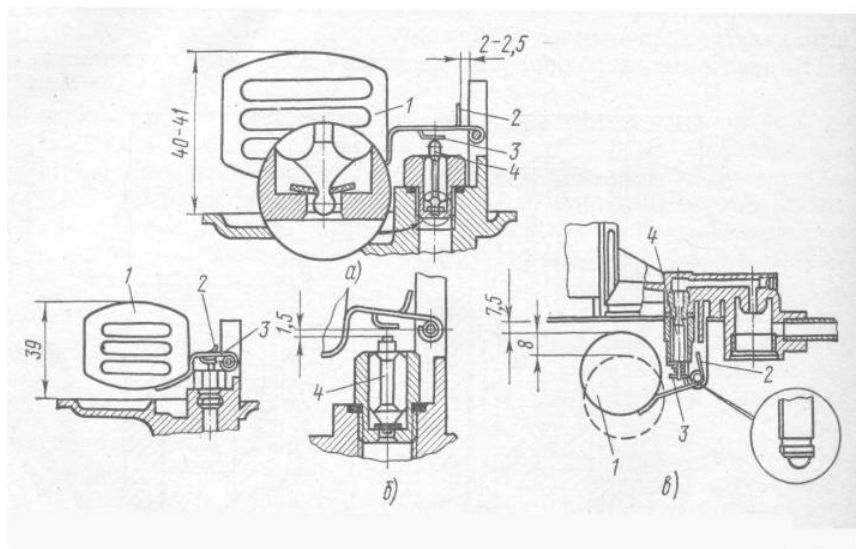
Регулировка уровня топлива в поплавковой камере карбюраторов: а – К-126Г, б – К-126Н, в – ДААЗ-2107; 1 – поплавок; 2 – ограничитель хода поплавка; 3 – язычок; 4 – запорная игла.
